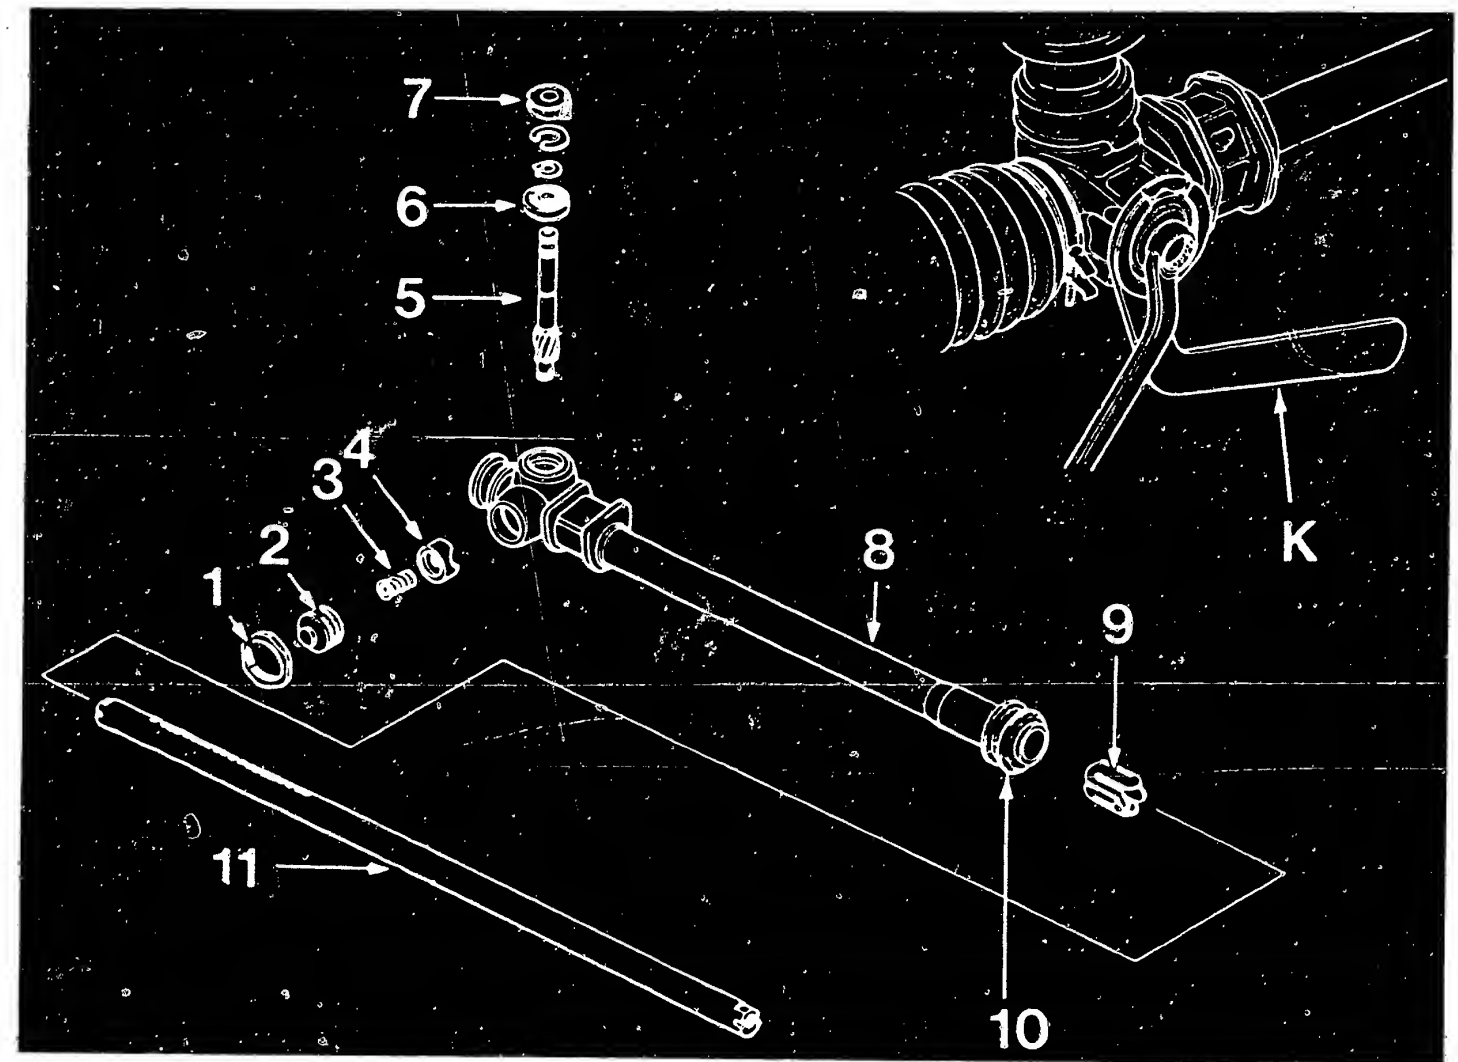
Zerlegtes Lenkgetriebe mit: 1 Kontermutter – 2 Einstellschraube – 3 Feder – 4 Andrückkolben – 5 Ritzel – 6 Kugellager – 7 Dichtring – 8 Gehäuse – 9 Führungsbüchse – 10 Lagerbüchse – 11 Zahnstange. Rechts oben: Einstellung des Zahnstangen-Führungskolbens mit dem Speziälschlüssel 07916-6920100 (K).
